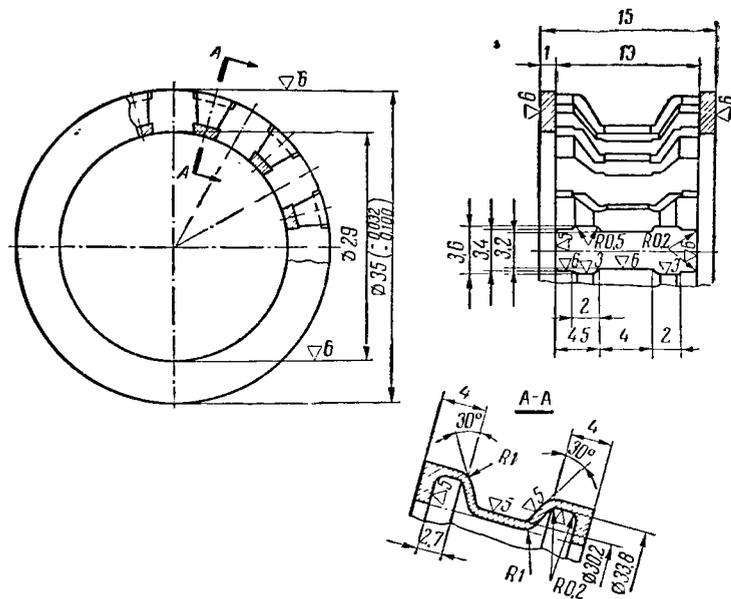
Стальной тонкостенный сепаратор подшипника большой головки шатуна (двигатель Кениг).
